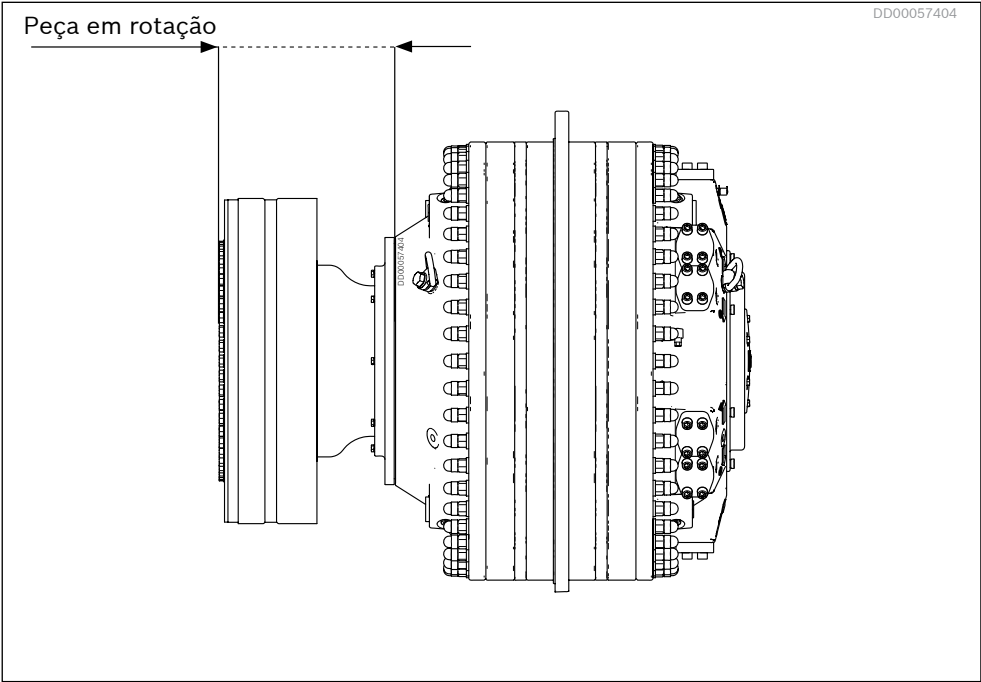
Peça em rotação, motor com adaptador de acoplamento
